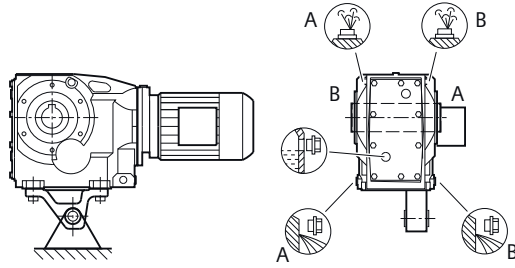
Konik dişli için montaj konumları K. Ayaklı model Boyutlar 39 - 109
